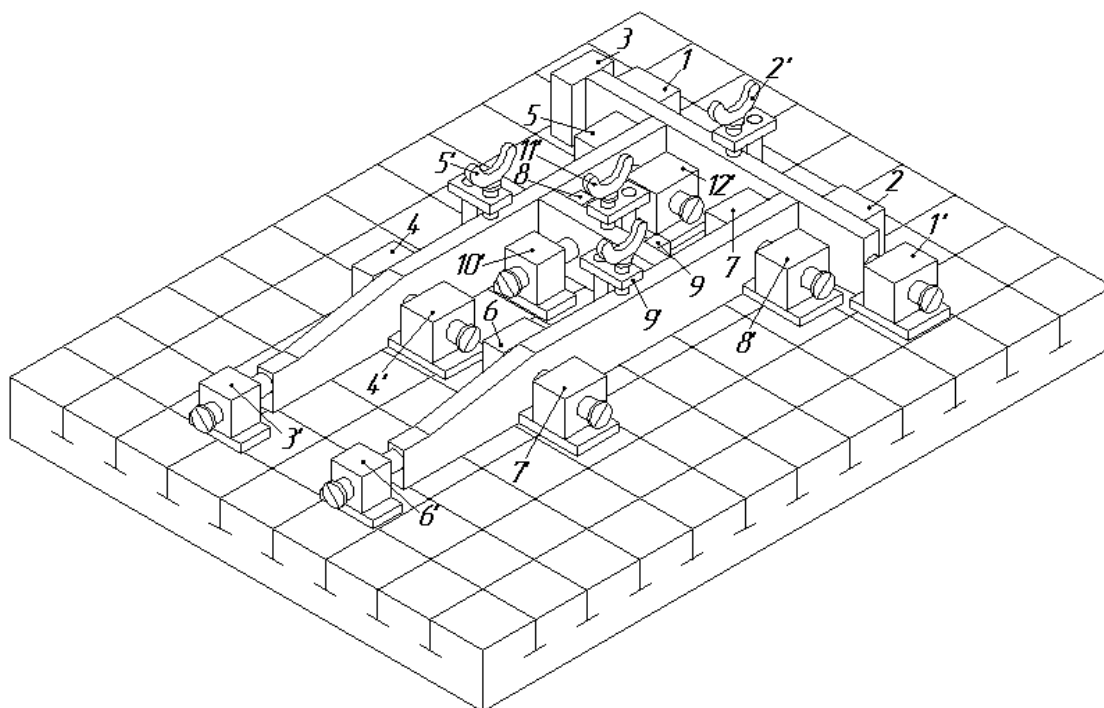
Базирование деталей и приспособлений на сборочно-сварочной плите:
